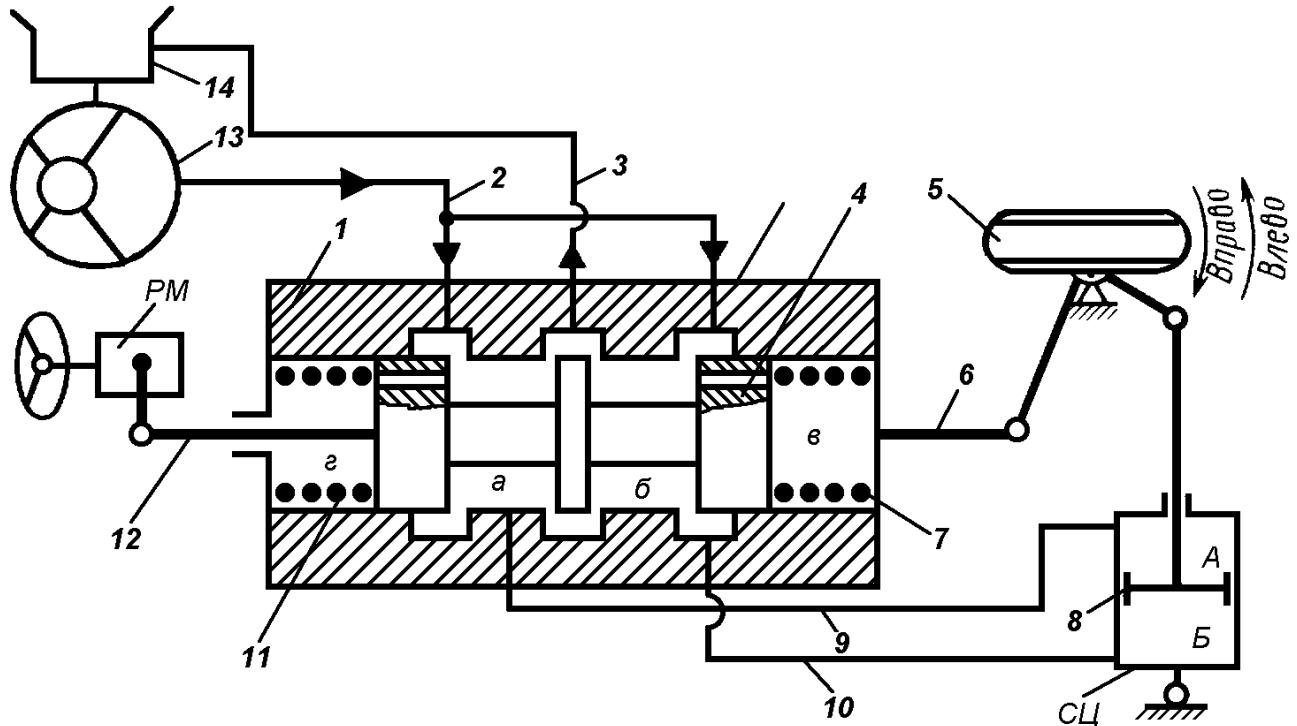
Схема гидроусилителя рулевого привода:
